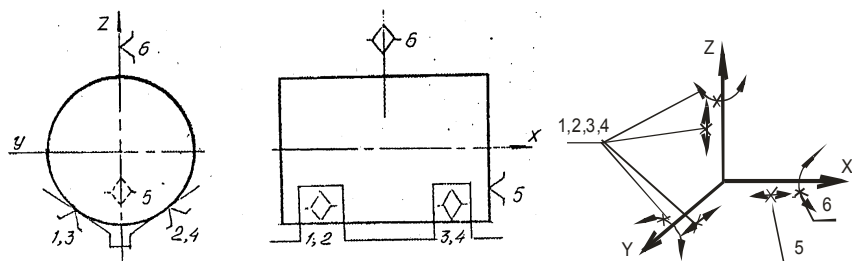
Теоретическая схема базирования заготовки типа вала по плоскости и наружной цилиндрической поверхности
